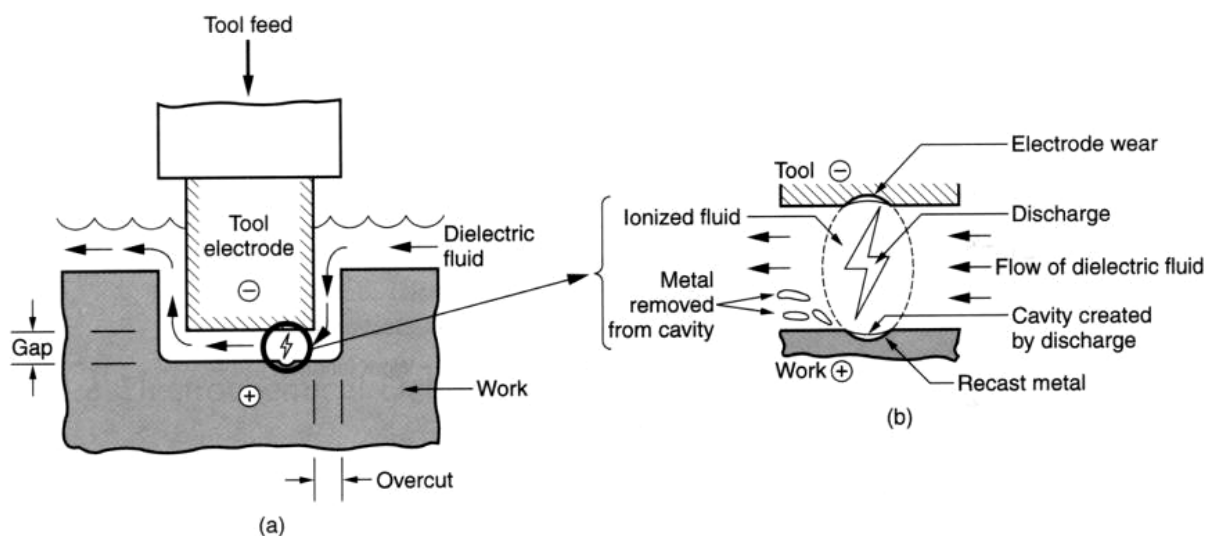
Usinage à l'électroérosion à l'électrode.
